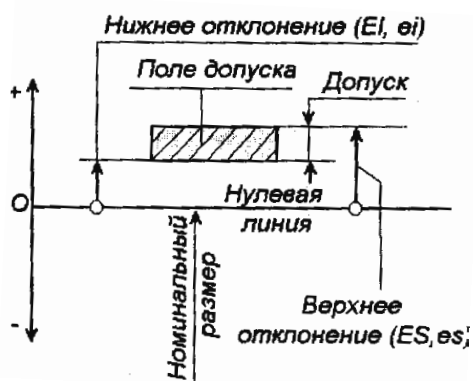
Расположение полей допусков вала и отверстия
